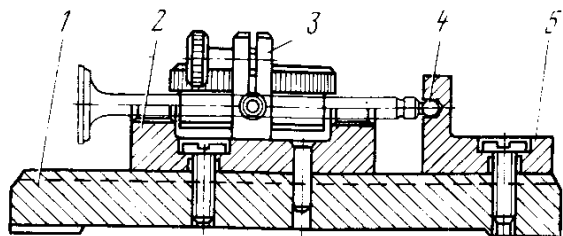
Приспособление для проверки клапана на concentricity рабочей фаски головки и стержня: 1—плита; 2—призма; 3—держатель; 4—шарик; 5—стойка; 6, 7—индикаторы
